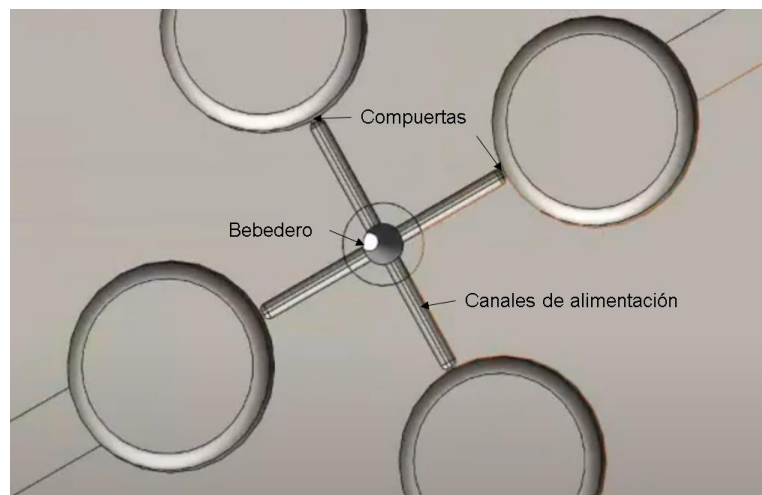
Sistema de alimentación de un molde de inyección. Fuente: Autor.
